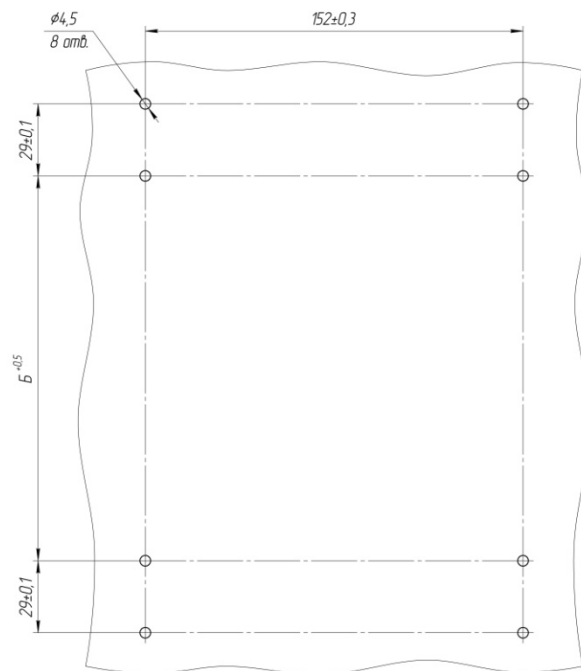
Габаритные и присоединительные размеры устройства РС83-АВ2 при внешнем монтаже, обеспечивающем его поворот влево/вправо
